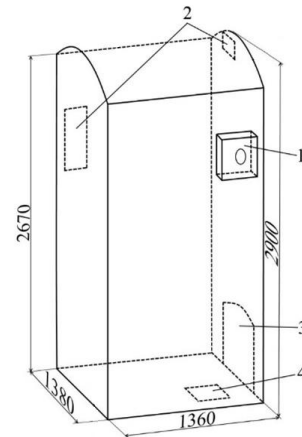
Схема топки котла (размеры в мм): 1 – короб форсунки; 2 – окна для подачи воздуха; 3 – вывод дымовых газов; 4 – летка ШЗУ.
